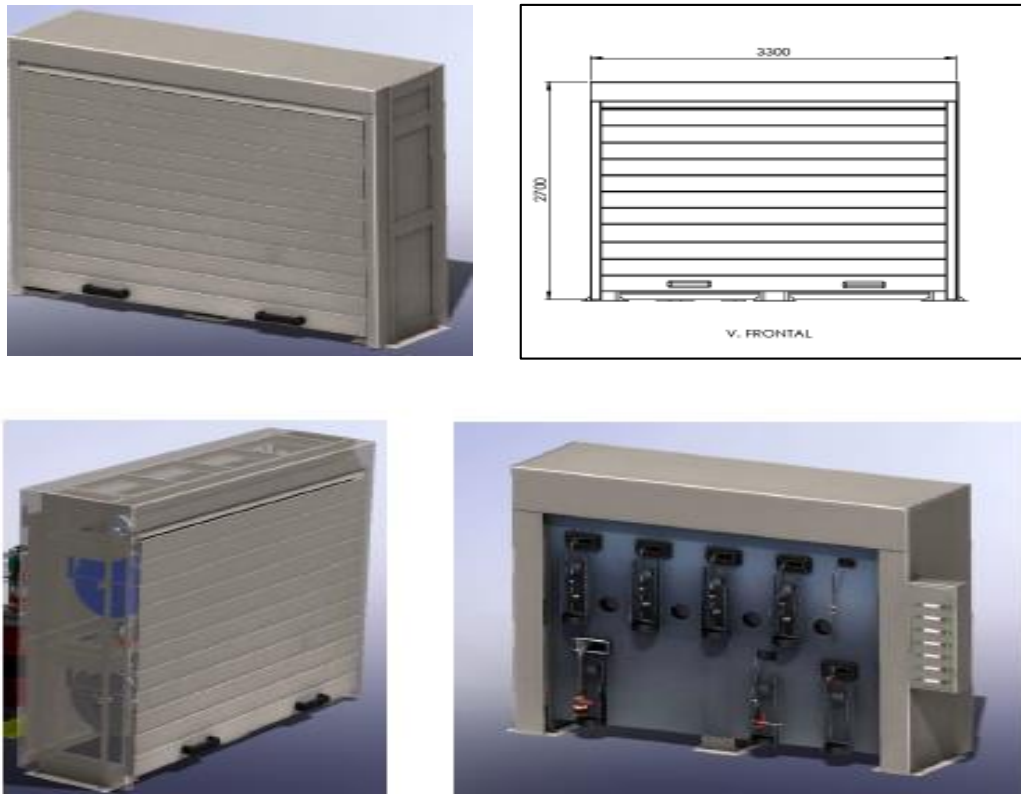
Módulo de lubricación encapsulado. Tomado de: Propuesta técnico-económica – Soltrak
